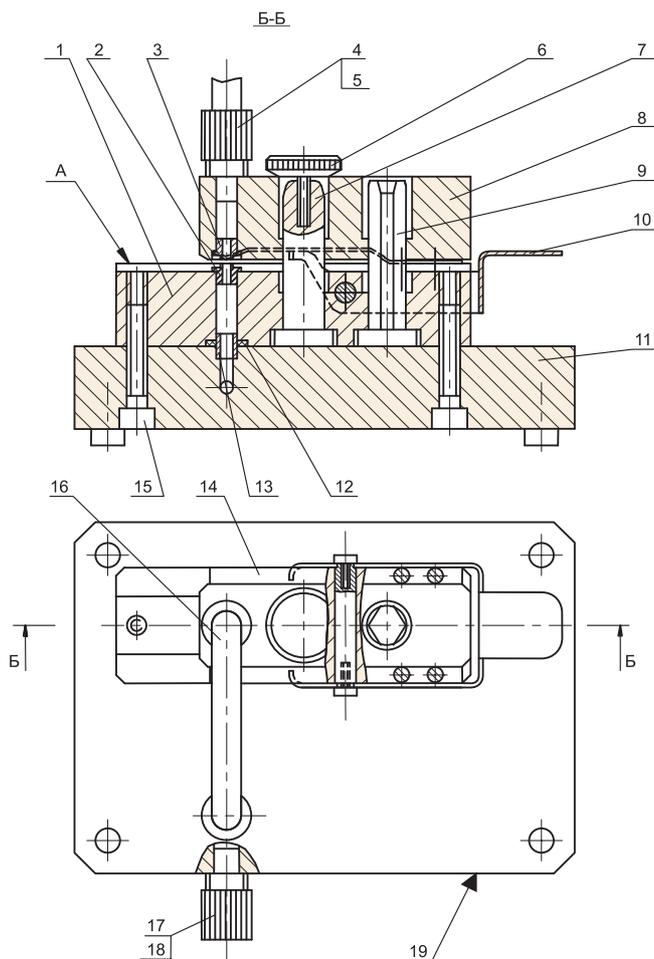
Конструктивное исполнение приспособления для имитации измерительных зазоров РЛПА.401262.044, где 1 – губка нижняя, 2, 3 – сопла, 4 – штуцер, 5 – гайка, 6 – винт, 7, 9 – направляющие, 8 – губка верхняя, 10 – рычаг, 11 – основание, 12 – прокладка, 13 – втулка, 14 – рычаг, 15 – винт, 16 – трубка, 17 – штуцер, 18 – гайка, 19 – место маркировки
